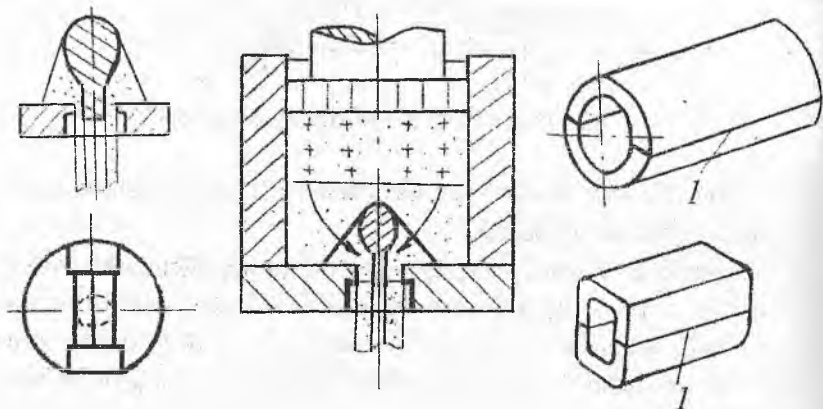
Схема прессования пустотелых профилей со сваркой
